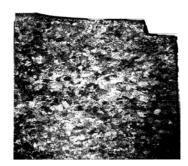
Макроструктура отливки вставки штампа для получения поковок вилки карданного вала (альтернативный вариант приготовления расплава)
